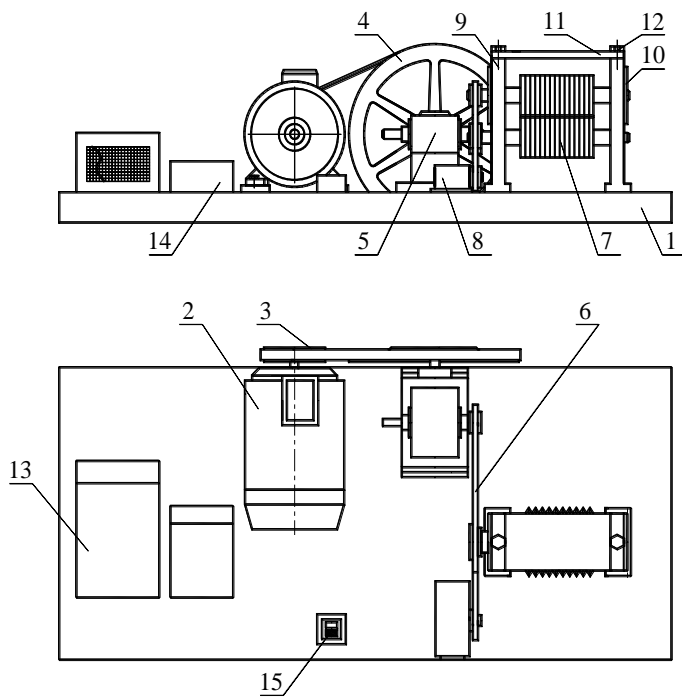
Експериментальна установка із зубчастими валками: 1 – плита; 2 – електродвигун; 3 – ведучий шків; 4 – ведений шків; 5 – черв’ячний редуктор; 6 – ланцюгова передача; 7 – зубчасті валки; 8 – натяжний пристрій; 9 – стійки; 10 – підшипникові вузли; 11 – пластина; 12 – болти для регулювання міжвалкової відстані; 13 – пристрій для вимірювання потужності; 14 – трансформатор; 15 – вмикач
